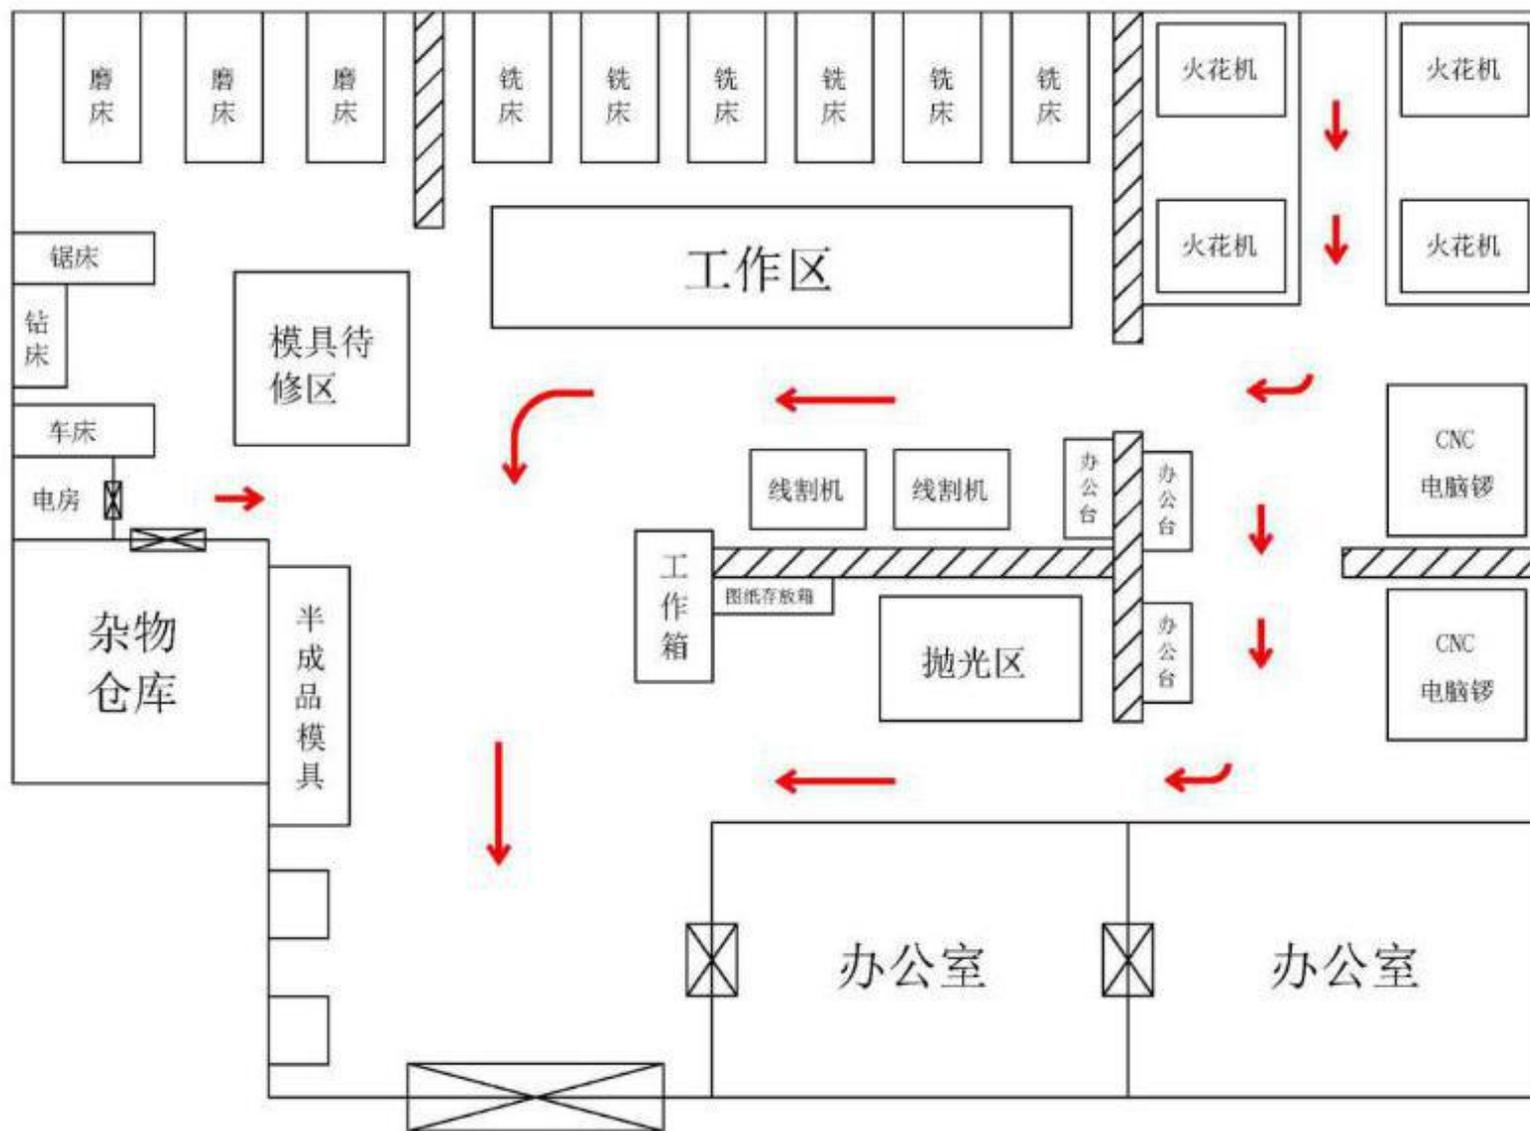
厂房平面布置图（工模车间，C 栋一层）
